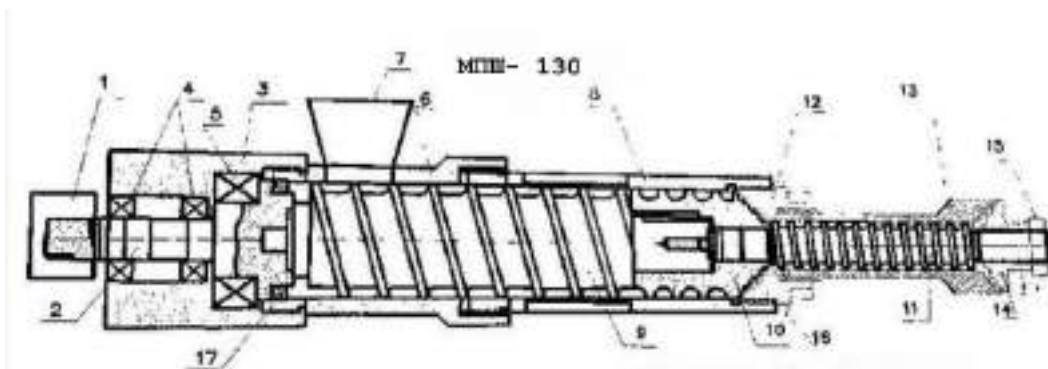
Робоча частина, зеєрний прес, шнекового преса ММШ-130
